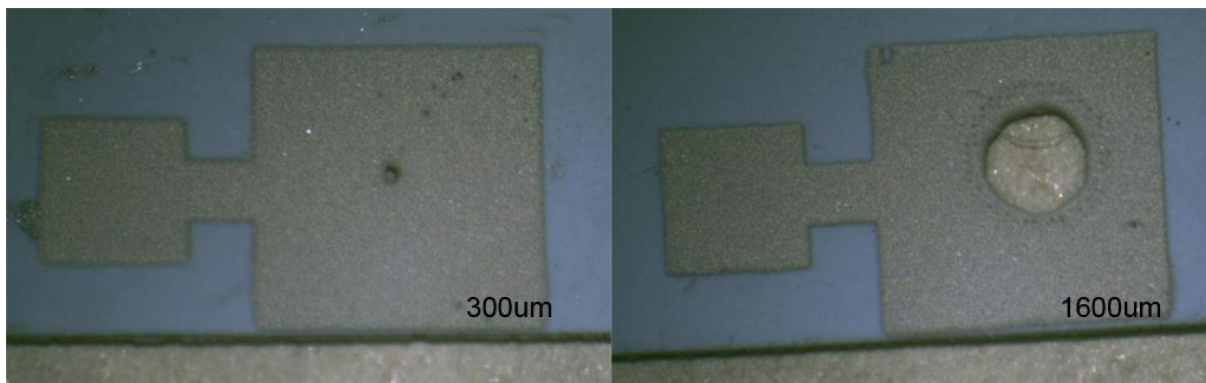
Súhrn všetkých rozmerov vyplnených dier
